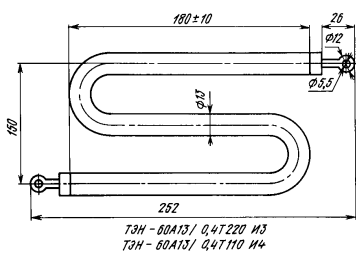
Габаритные, установочные и присоединительные размеры ТЭНов 60А13/0,4Т110И4; 60А13/0,4Т220И3
